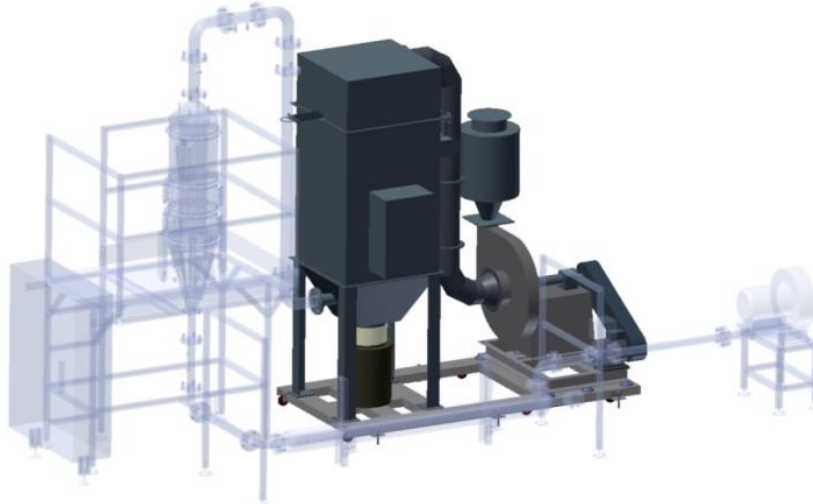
Esquema 3D de la planta piloto con el sistema de depuración de aire resaltado.
